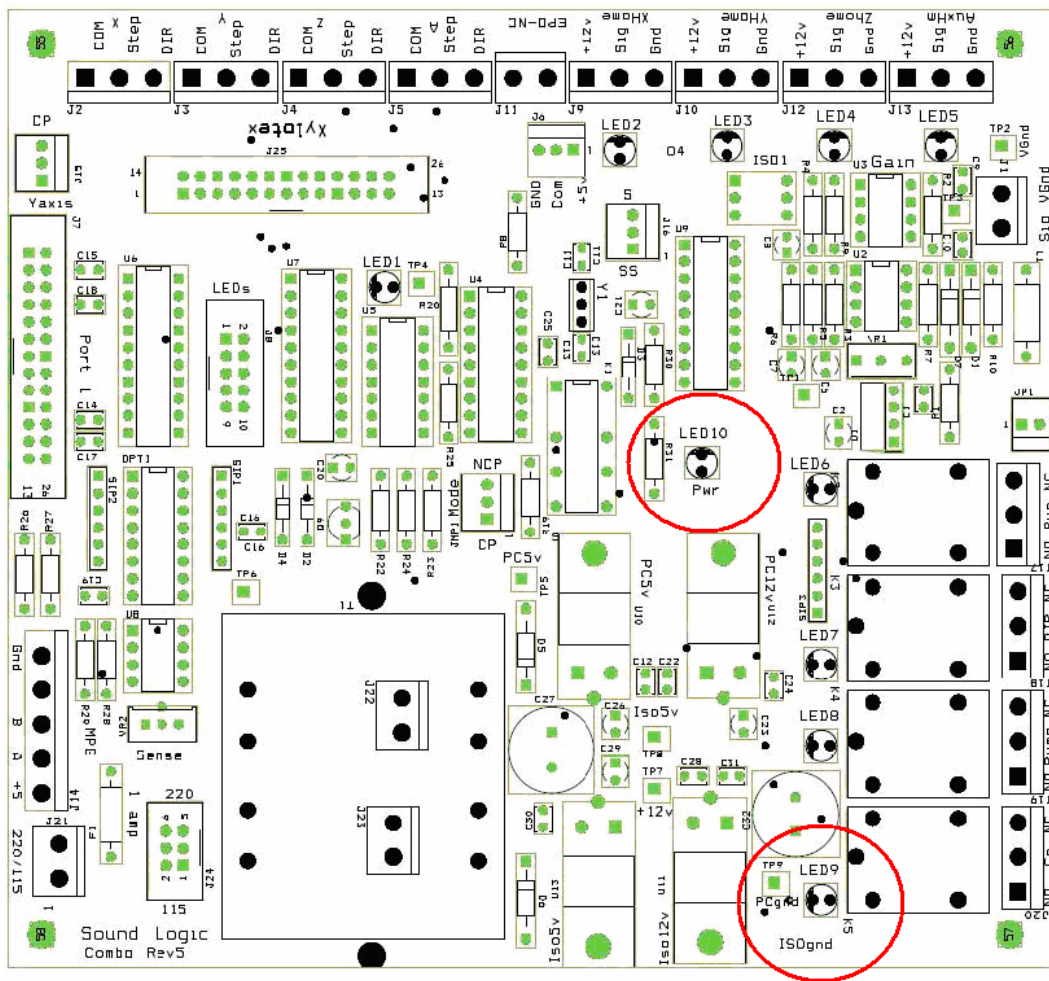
Vista superior de la tarjeta interface Breakout Board Rev. 5
